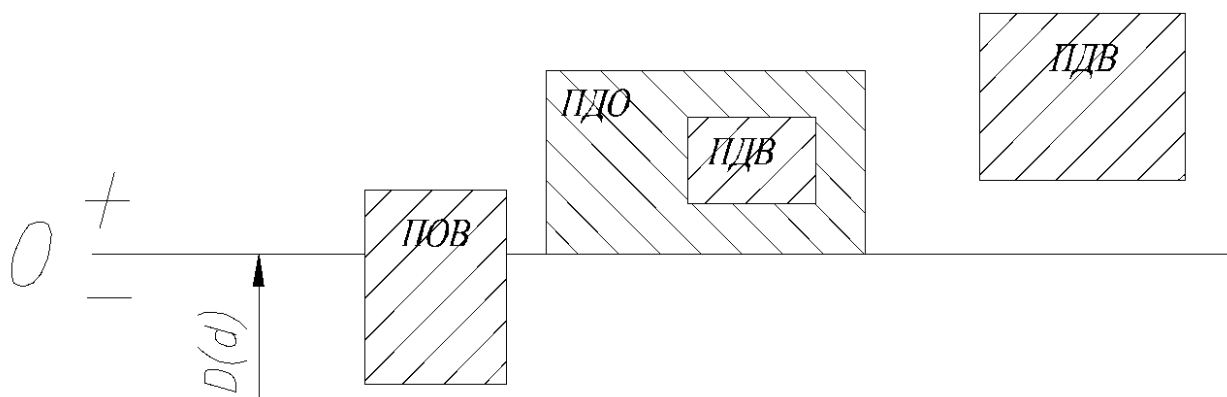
Схема розташування полів допусків перехідного з'єднання
